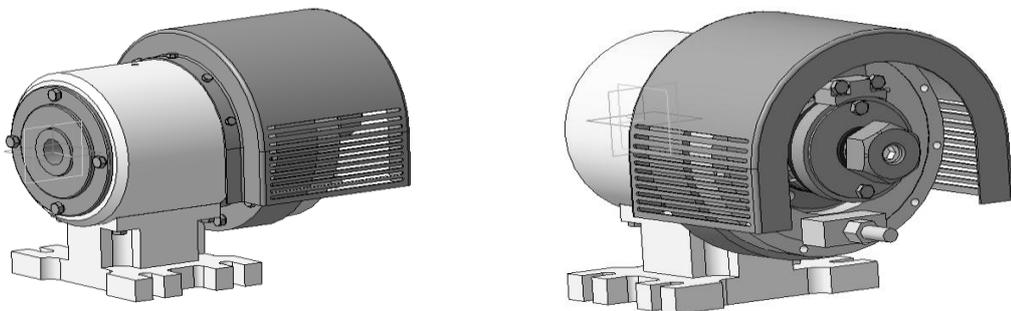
Разработанная 3D модель бабки шлифовально-заточного станка с ЧПУ
